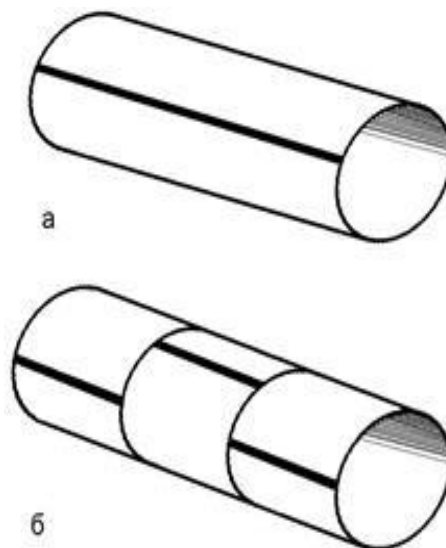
Схеми виготовлення циліндричної частини ємностей:
